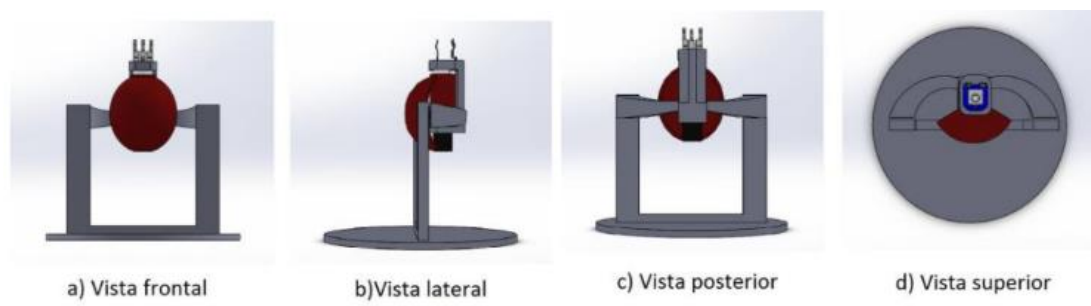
Diseño mecánico enfocado a utilizar el menor espacio posible en el que toma en cuenta el motor que pueda mover al sensor de posición para poder determinar la posición actual del ojo. Diseño CAD en distintas vistas. [13]
